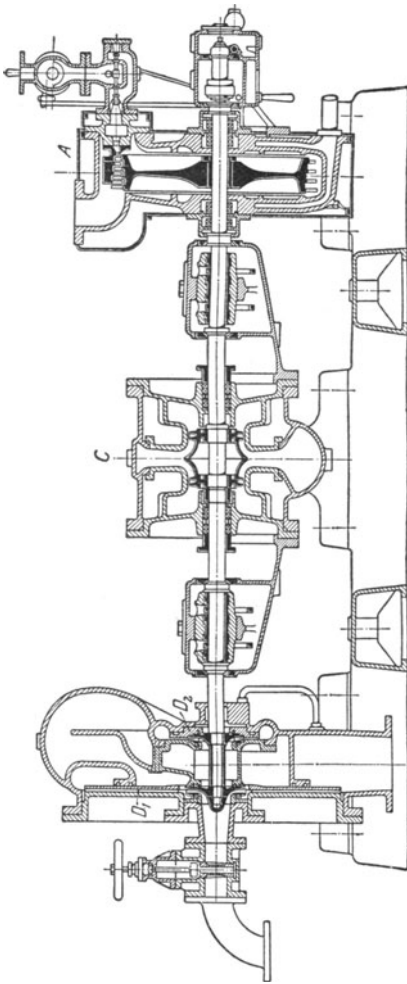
Schnitt durch die Pumpen eines Oberflächkondensators mit Turbinenantrieb. Bauart der A. G. Berlin.
